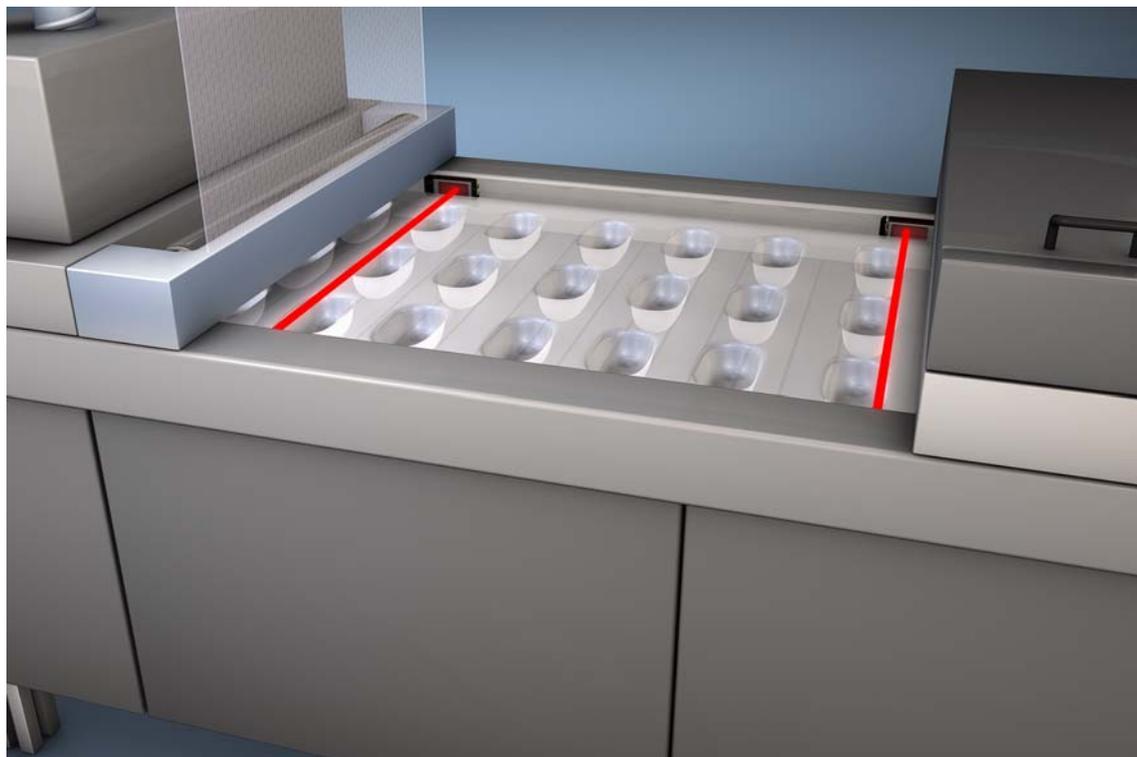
Protection contre l'intervention sur une empaqueteuse
